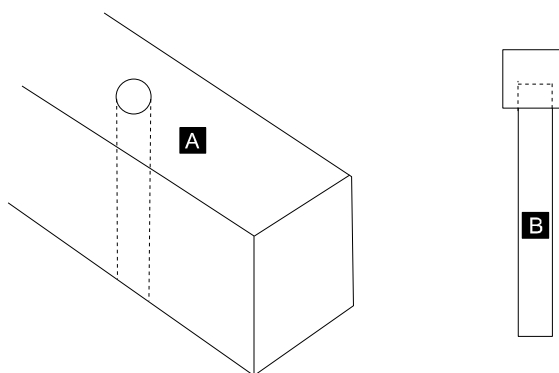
pièces de la jambe assemblée vue de côté et de haut
